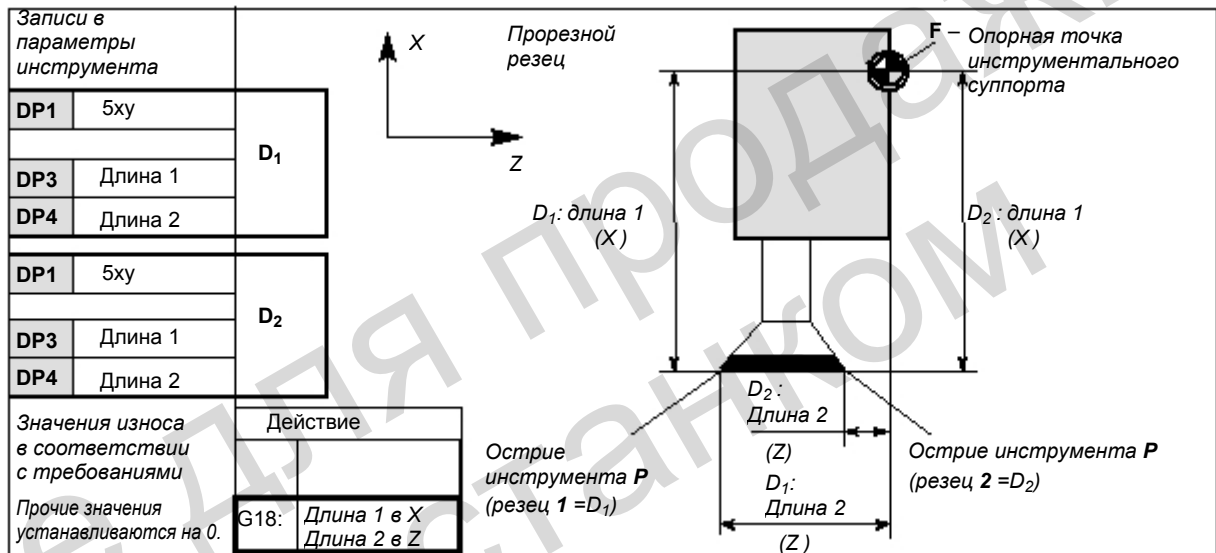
Токарный инструмент в с двумя резцами – коррекция длин
